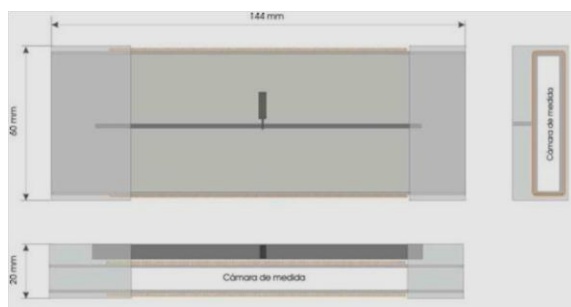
Dibujo acotado de la bobina captora y la posición del sensor.
